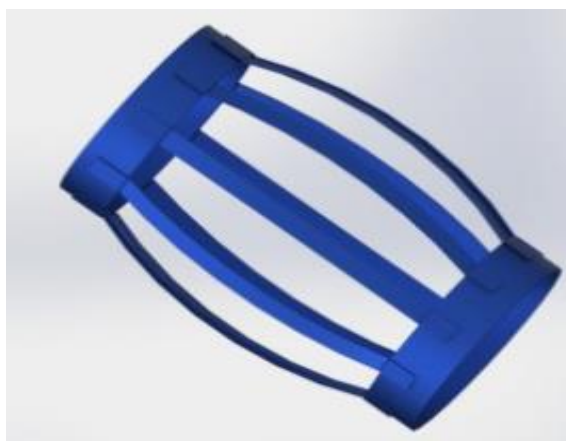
Центратор пружинный сварной ПЦС
